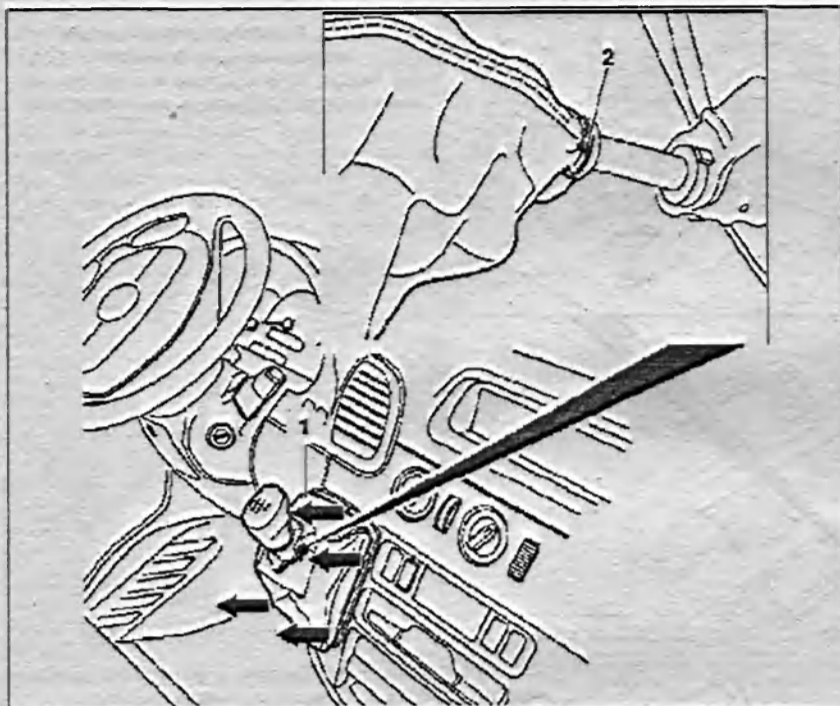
Снятие и установка чехла рычага переключения передач:
